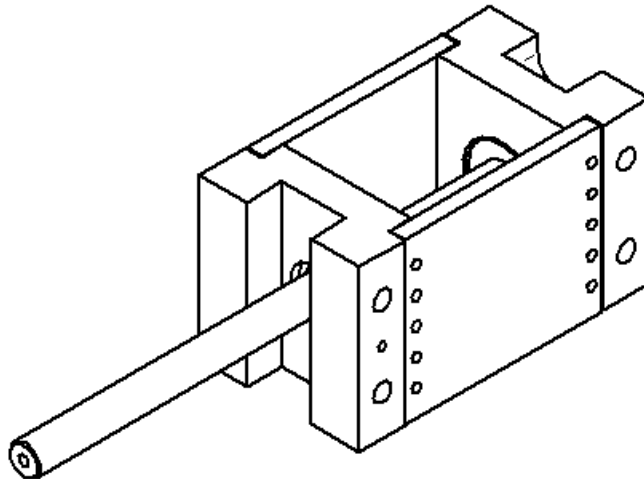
Vista isométrica del diseño de rotor de prueba.
